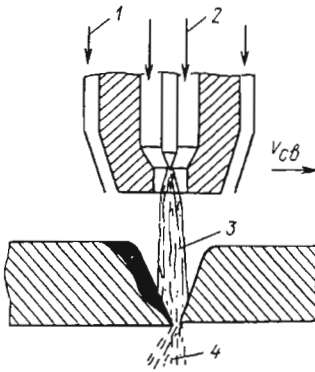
Схема плазменной сварки проникающей дугой:
